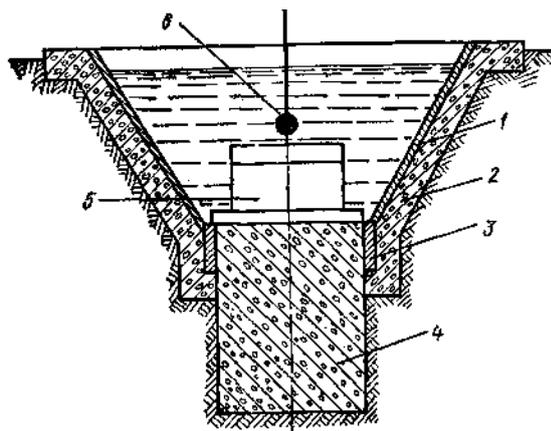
Схема бассейна конструкции Харьковского авиационного института; 1 — стальная обшивка; 2 — бетонный бассейн; 3 — гидроизоляция; 4 — заглубленный фундамент; 5 — штамп; 6 — заряд ВВ.
